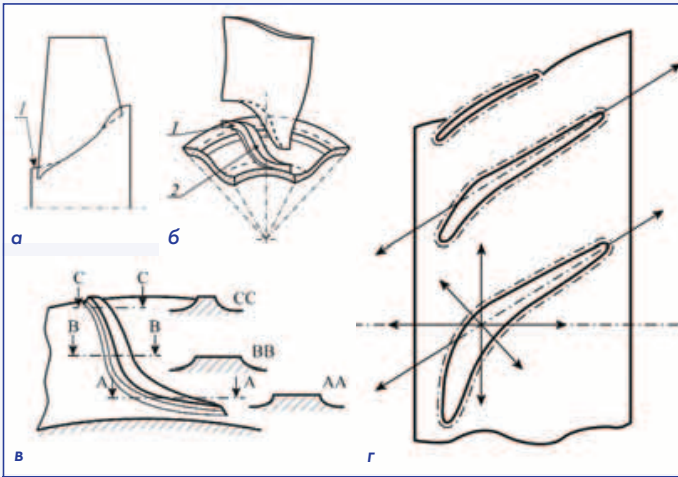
Ремонт монокоилс с ободом сложной формы: а, б) схема подготовки свариваемых поверхностей; в) привулочный участок обода; г) схема движения при сварке трением
